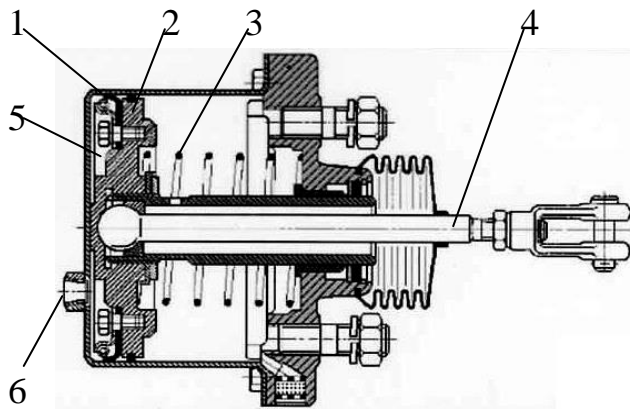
а. Конструкция поршневой тормозной камеры прямого действия: 1 – корпус; 2 – поршень; 3 – возвратная пружина; 4 – шток; 5 – рабочая полость; 6 – отверстие для подвода сжатого воздуха от тормозного крана
